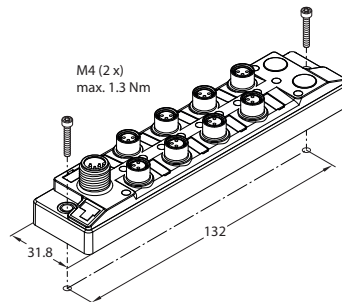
Gerät auf Montagefläche befestigen (Beispiel: TBIL-S3-...)
